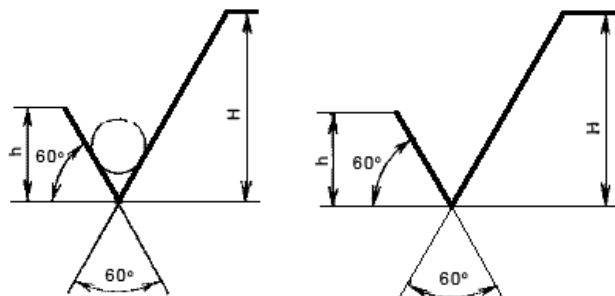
Знаки условного обозначения шероховатости поверхности
